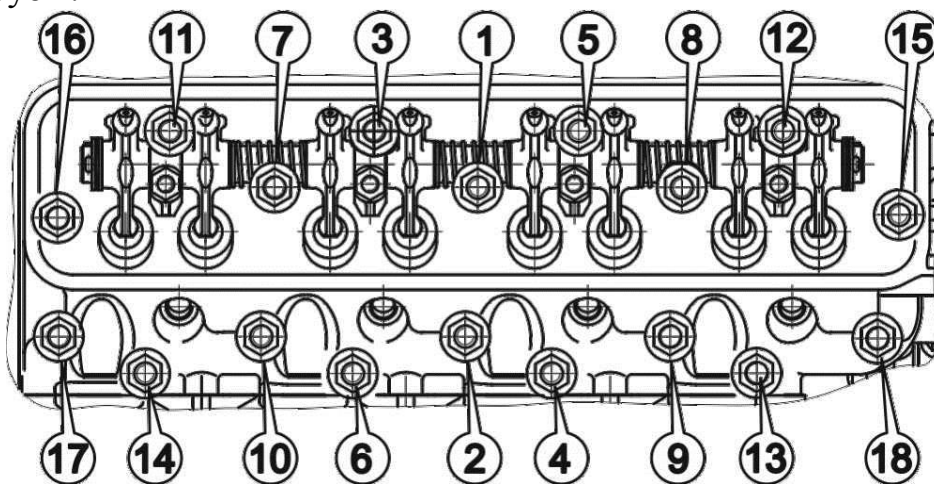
Порядок подтяжки гаек крепления головок цилиндров
